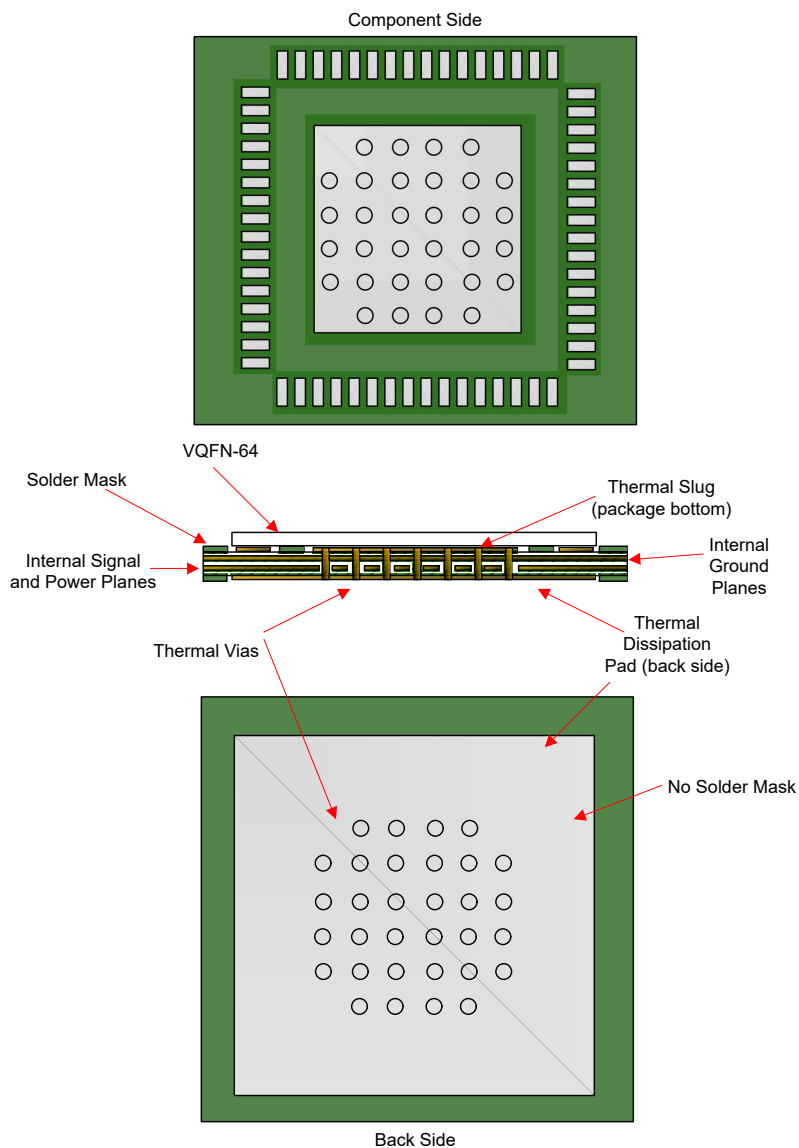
可实现热可靠性的通用 PCB 接地布局 (建议 8 层以上)
